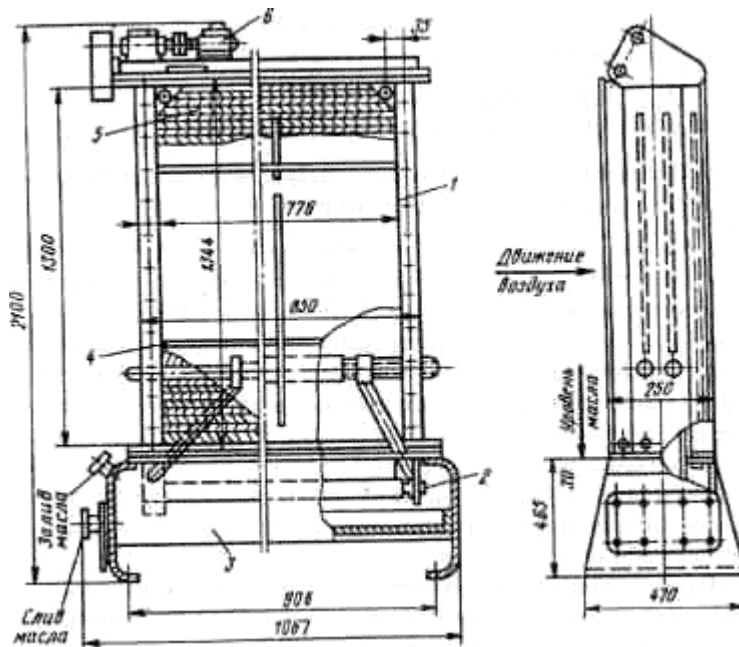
Самоочищающийся масляный фильтр с пружинной сеткой (номинальная производительность 10000 м³/ч): 1 — корпус; 2 — натяжное устройство; 3 — бак для масла; 4 — ограничитель сетки; 5 — пружинные сетки; 6 — привод сеток.
